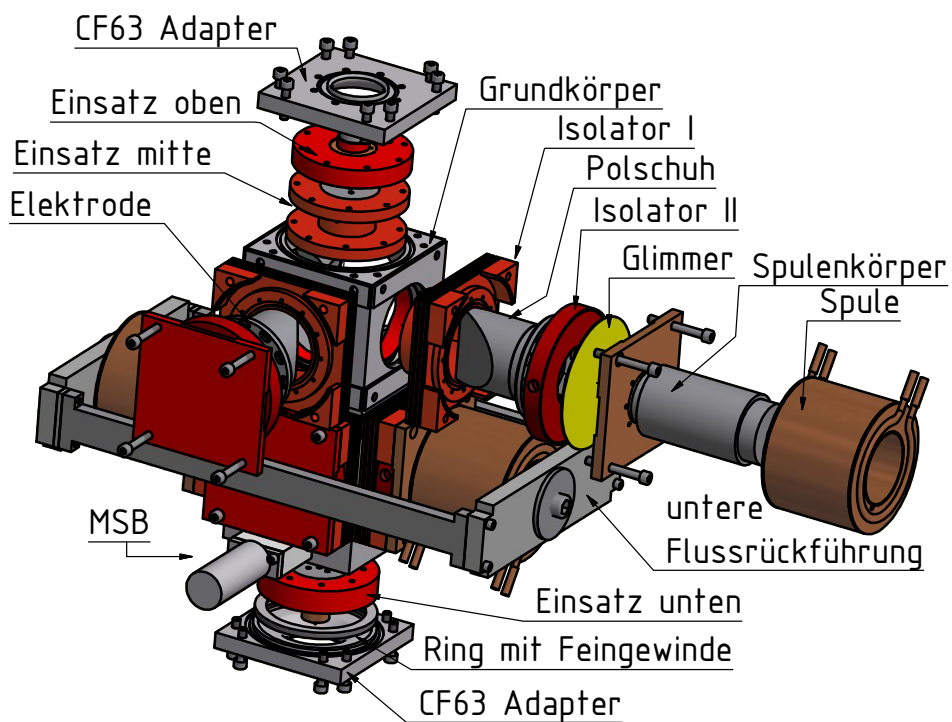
CAD Explosionsansicht des Massenseparators. Die obere Flussrückführung ist nicht eingezeichnet.
